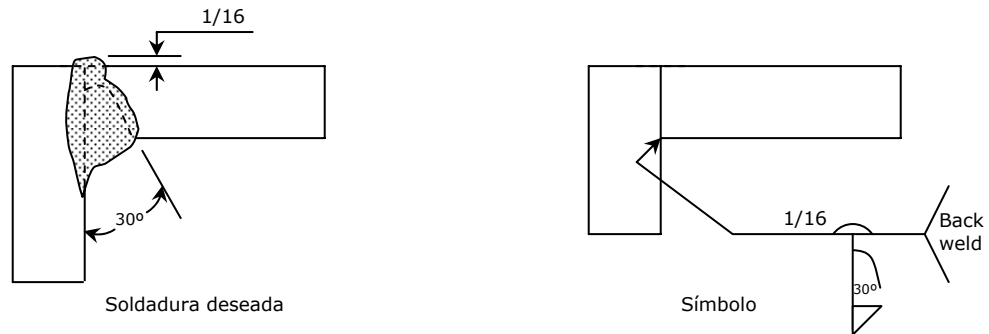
Símbolo de soldadura combinada
